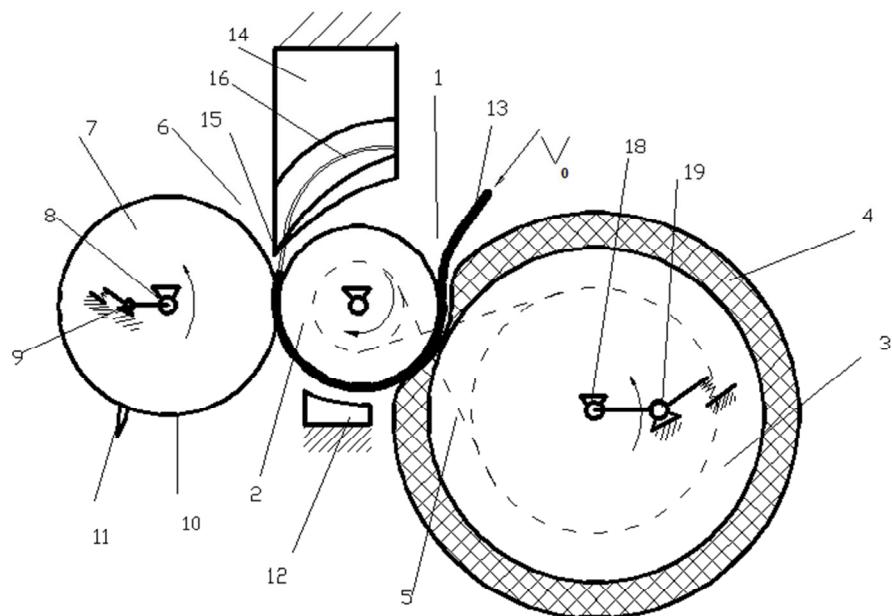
Общая схема способа изготовления разрезных полимерных колец
